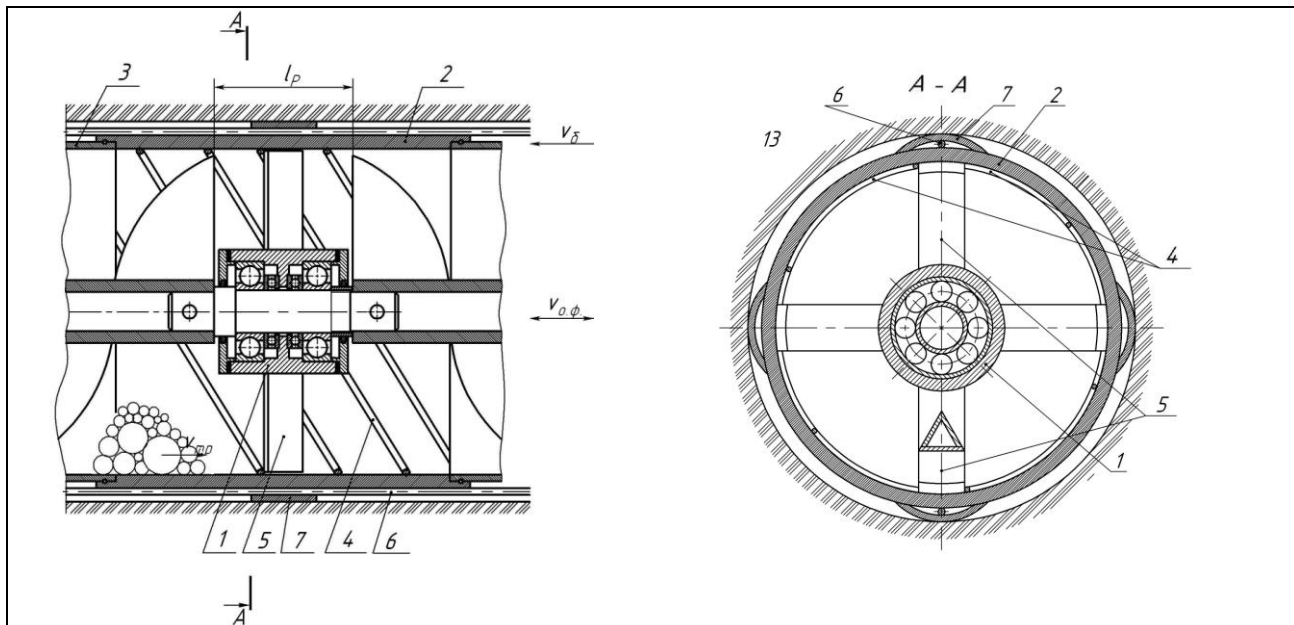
Конструкция центрирующей опоры шнекобурового става: 1 – подшипниковый узел; 2 – вкладыш-замок; 3 – обсадная труба; 4 – винтовая линия; 5 – опорный луч; 6 – вал; 7 – опорно-направляющий кожух
